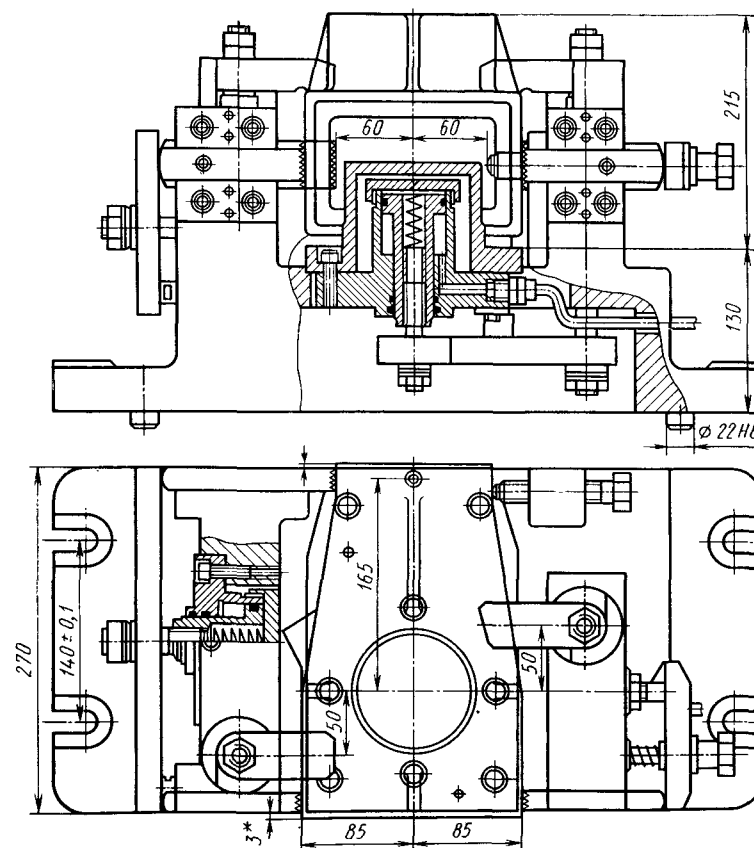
Приспособление для фрезерования плоскостей корпуса компрессора 9—1662
